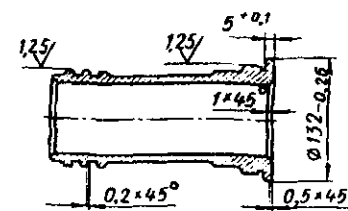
Наладка полуавтомата 1А730 для обработки гильз цилиндров двигателей
